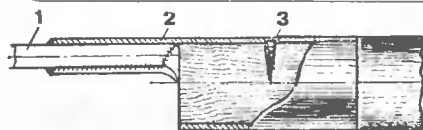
Сварное соединение рыхлителя с ручкой:
